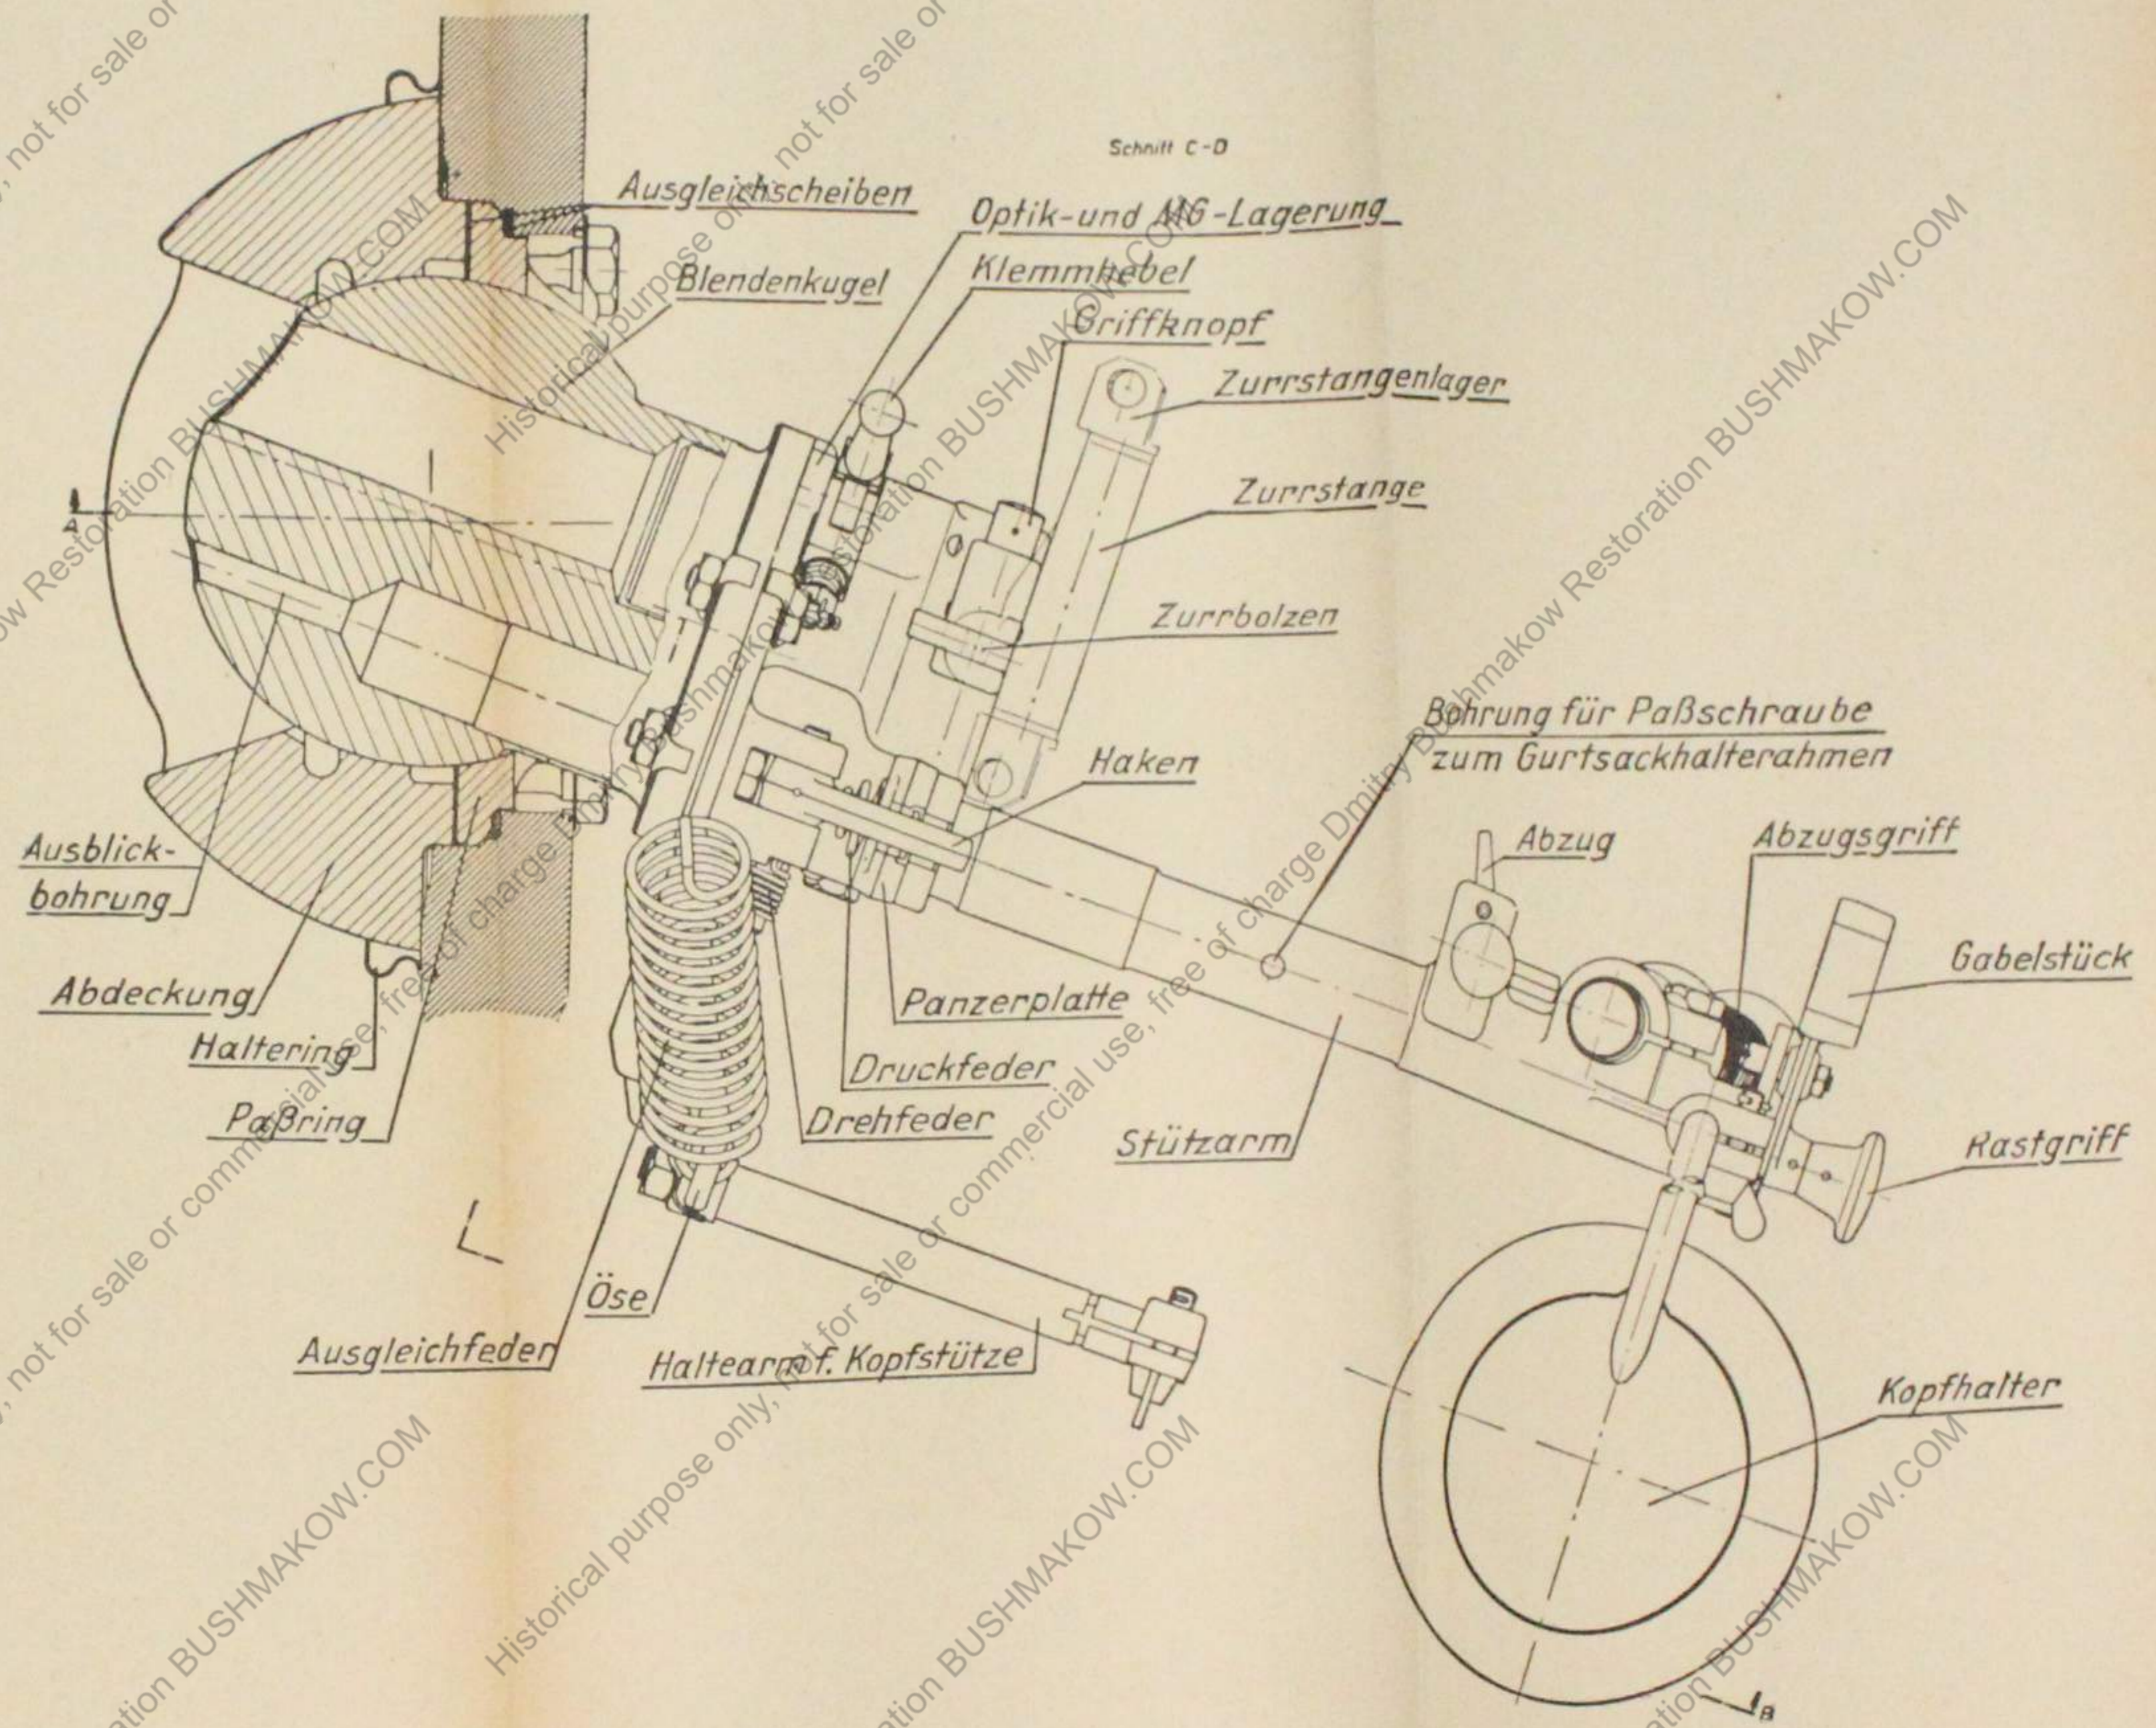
Augensblende 50, gezurrt, Schnittbild, Grundriß
